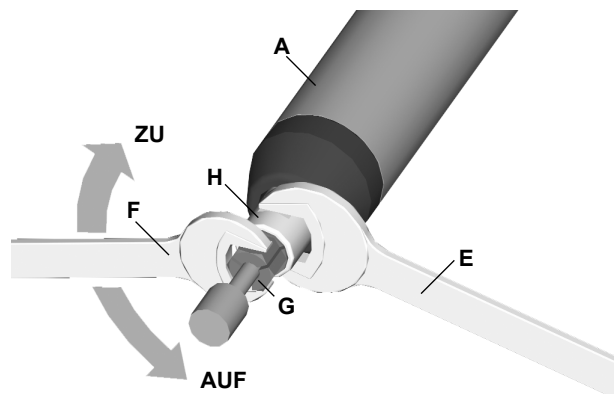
Werkzeugwechsel R 4102 / R 4105
